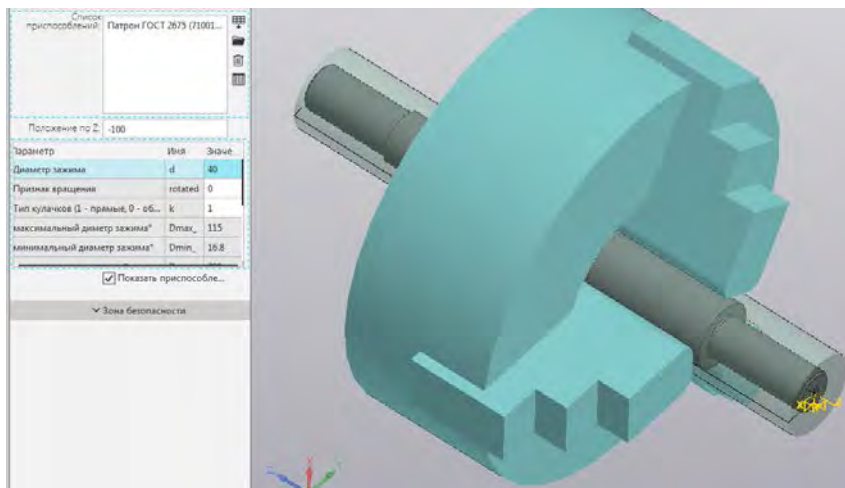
Создание приспособления для закрепления заготовки и задание его положения в первом установе
